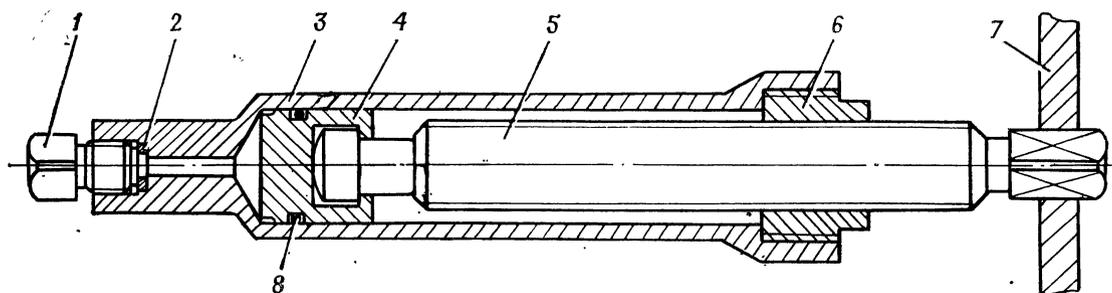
Приспособление 41.130 для зарядки накатника жидкостью:
